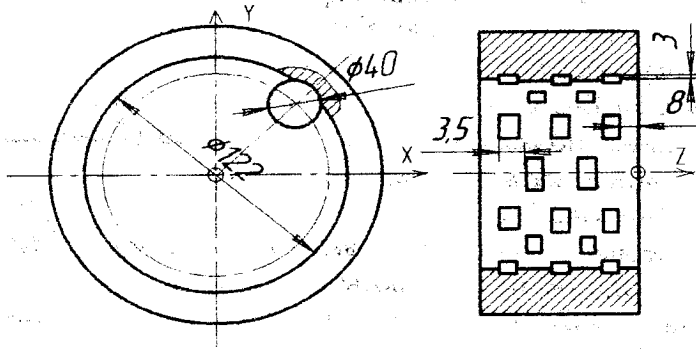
Ескіз для прикладу програми фрезерування лунок шляхом радіального врізання дисковою фрезою
